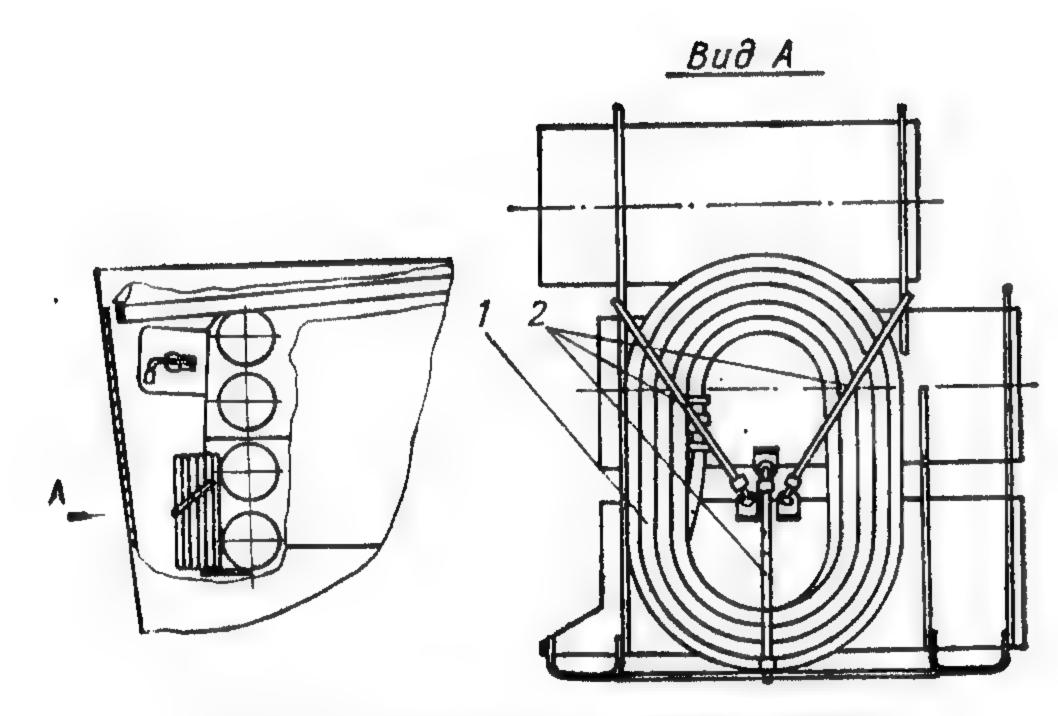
Размещение удлинителя шнура: 1— удлинитель шнура; 2— шнур резиновый
